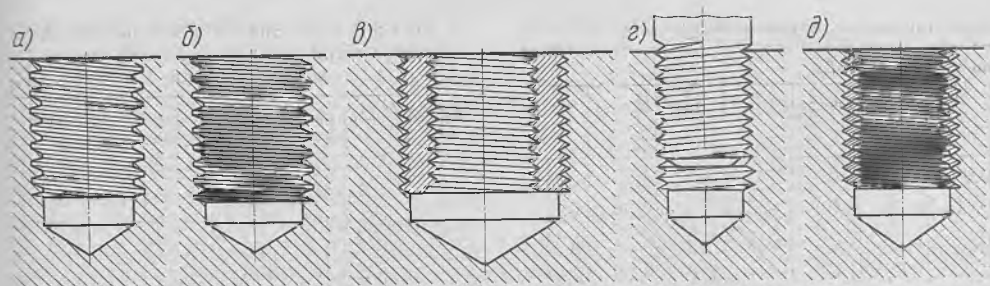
Способы ремонта резьбовых соединений: а — заварка отверстий с изношенной резьбой с последующим нарезанием резьбы номинального размера; б — нарезание резьбы увеличенного размера (под ремонтный размер); в — установка свертыша; г — стабилизация резьбовых соединений полимерной композицией; д — установка спиральной вставки
